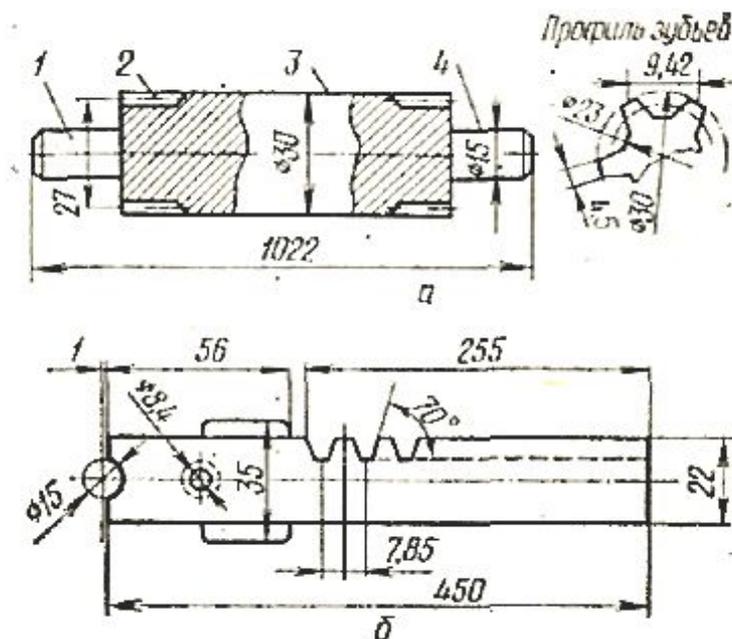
Товарный валик (а) и зубчатая рейка (б)
